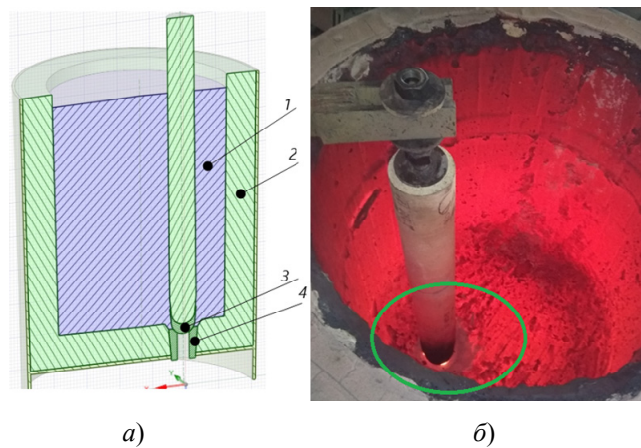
Стопорный литейный ковш емкостью 4 т: а – схема: 1 – расплав; 2 – футеровка ковша; 3 – стопорная пробка; 4 – стопорный стакан; б – проверка правильности установки стопорной пробки с применением засыпки кварцевого песка
